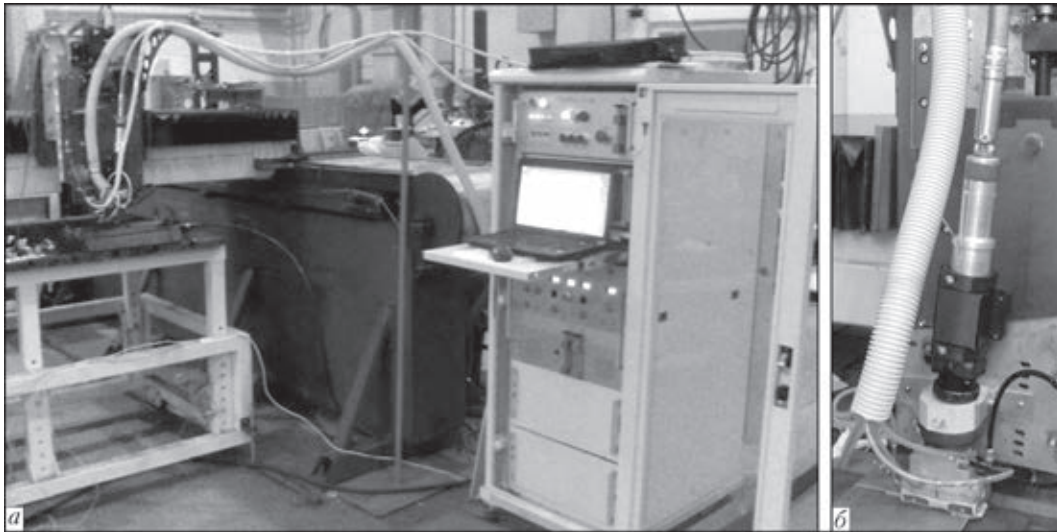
Внешний вид комплекса лазерно-микроплазменной сварки (а) и гибридного плазмотрона (б)
